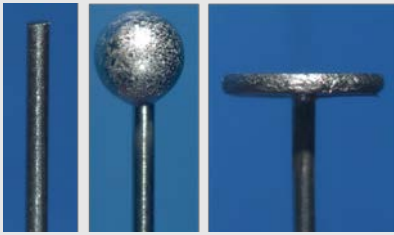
(v.l.n.r.): Ausgangshalbzeug, Durchmesser 0.5 mm. Zwischenform. Umformerzeugnis
